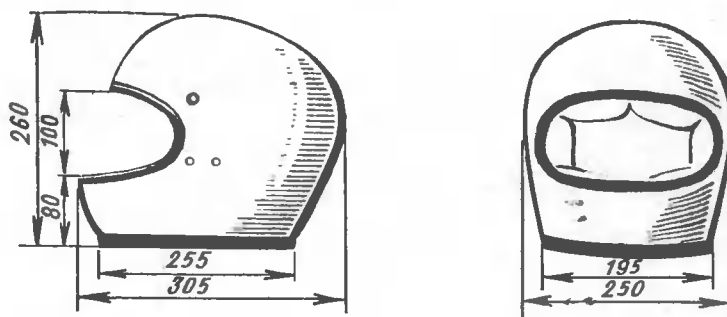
Основные размеры и внешний вид простейшего шлема «интеграла».
